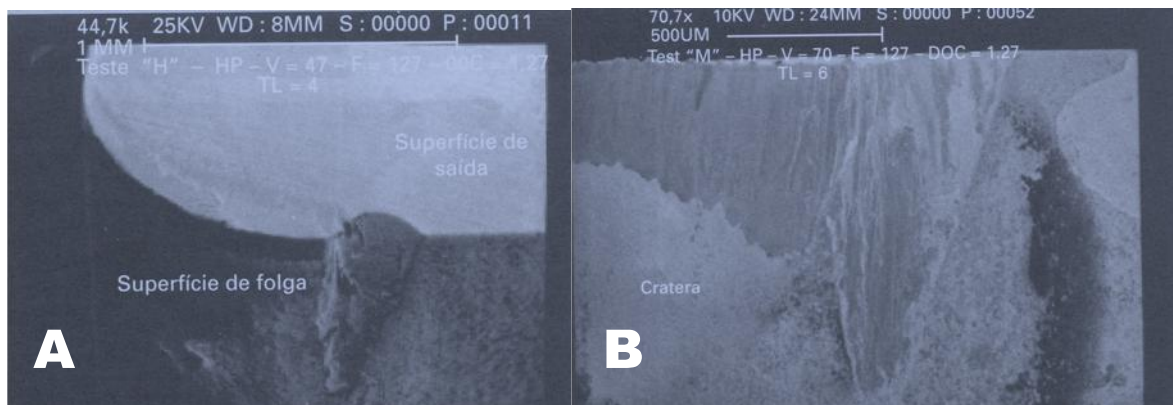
A – Desgaste de entalhe observado em uma ferramenta de metal duro K20 após usinagem de Inconel 901 e B - vista do desgaste de entalhe na superfície de folga (MACHADO et al., 2009, p. 263 e 265)
